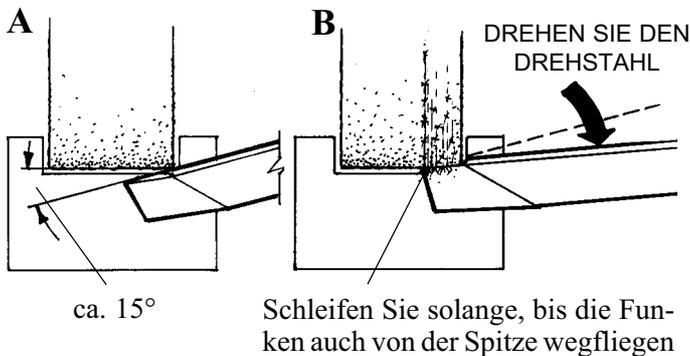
Schleifen der Schräge auf Seite 3 des Stahls
